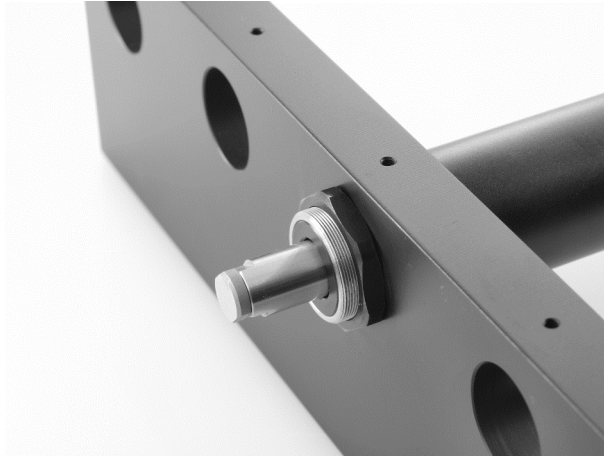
Beispiel für den Einbau eines Linearaktors (hier: ein M-235)
